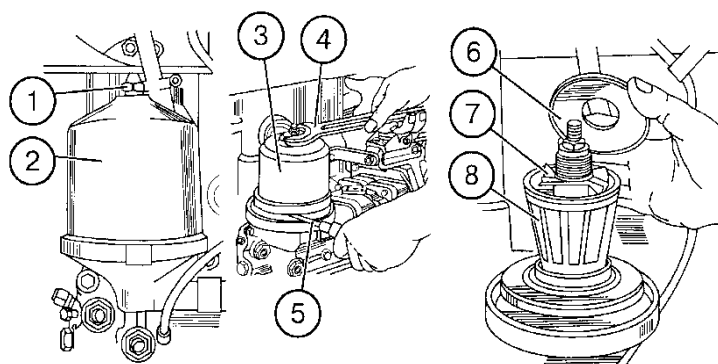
Очистка ротора центробежного масляного фильтра:
